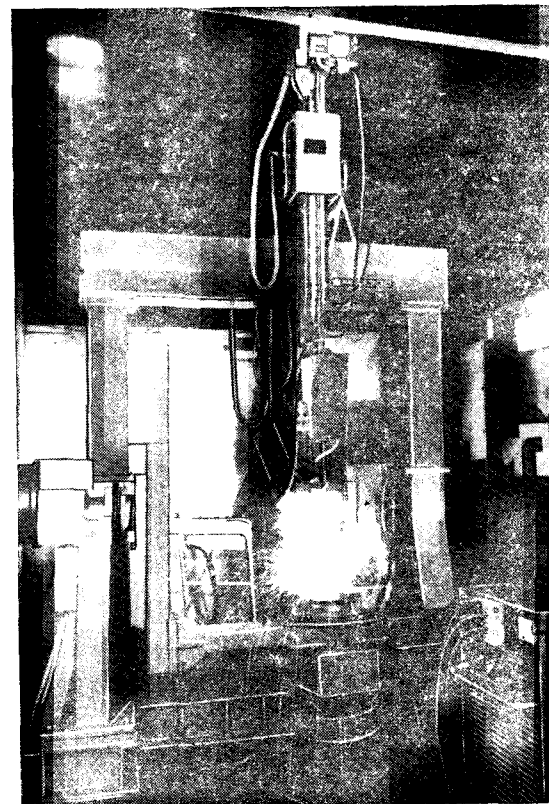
Портальный ПР для дуговой сварки ВНИИЭСО
